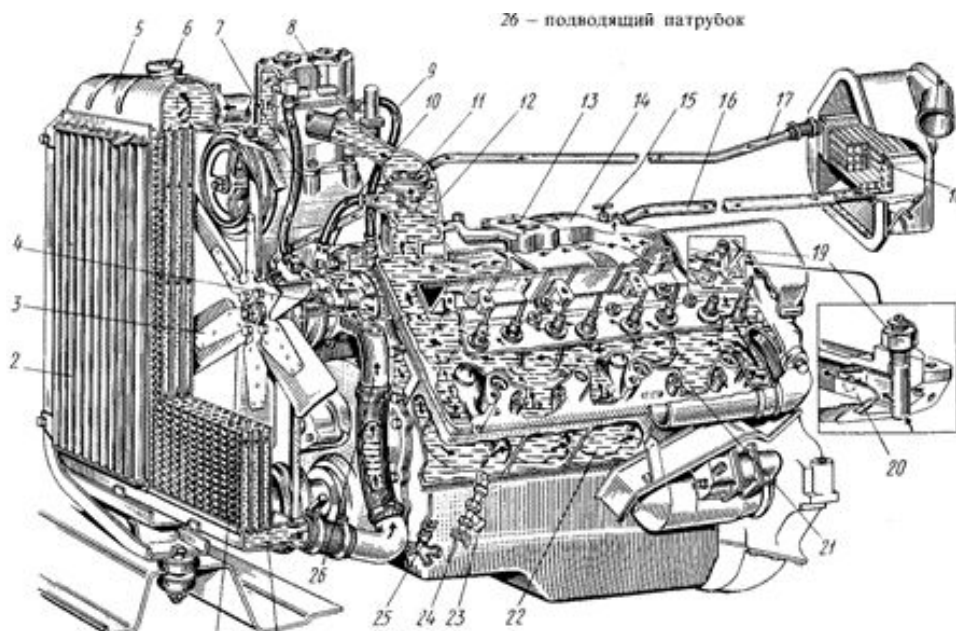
Система охлаждения двигателя автомобиля ЗИЛ-130
